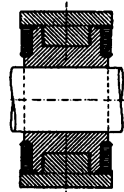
Feldmagnet mit aufgeschraubten Polen.
